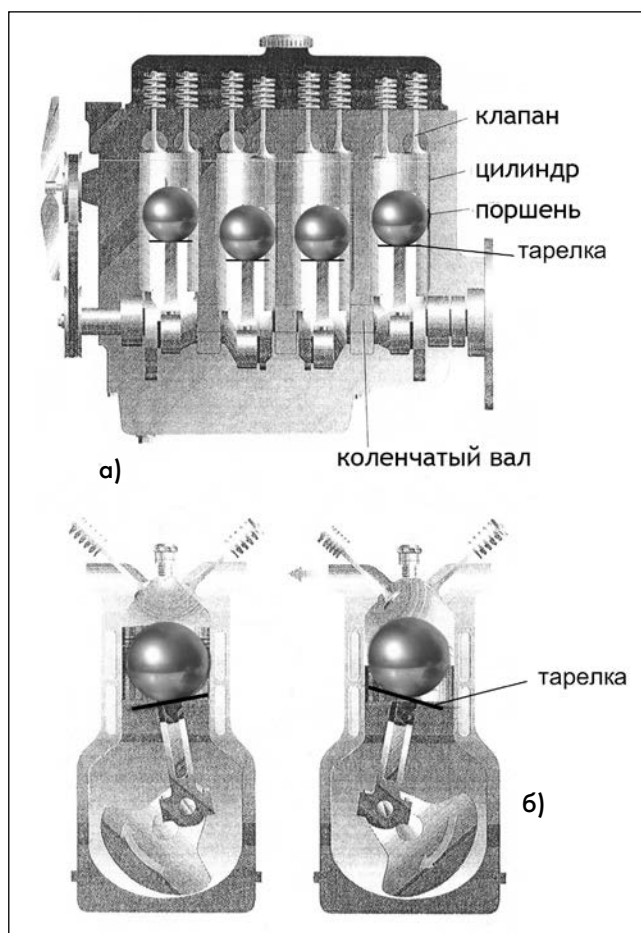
Двигатель внутреннего сгорания с шаровыми поршнями — а), положения кривошипного вала — б)
